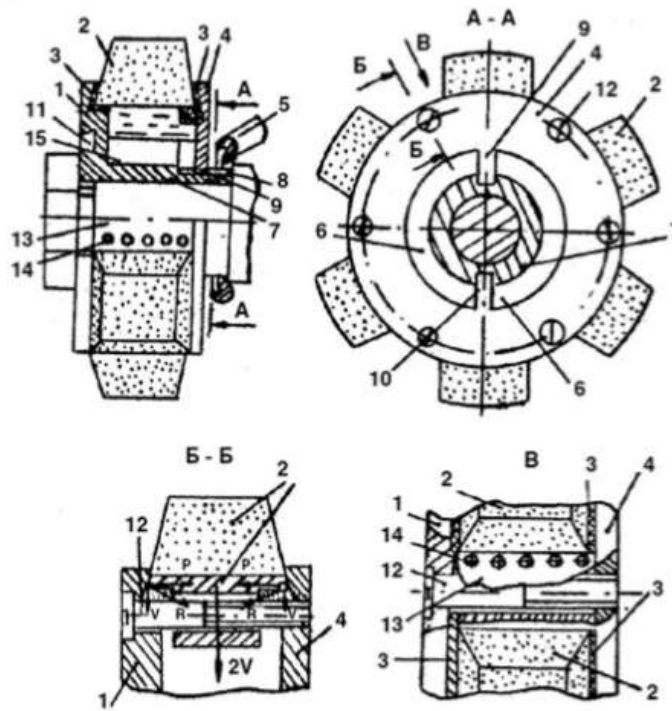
Збірний абразивний круг з кріпленням ріжучих сегментів по чотирьох сторонах: 1 - корпус; 2 - абразивний сегмент; 3 - пружний елемент; 4 - кришка; 5 - трубопровід; 6 - щілина; 7 - посадкова втулка; 8 - поздовжній паз; 9, 10 - радіальні ділянки; 11 - кільцева канавка; 12 - гвинт; 13 - планка; 14 - отвір; 15 - приймальна порожнина.
